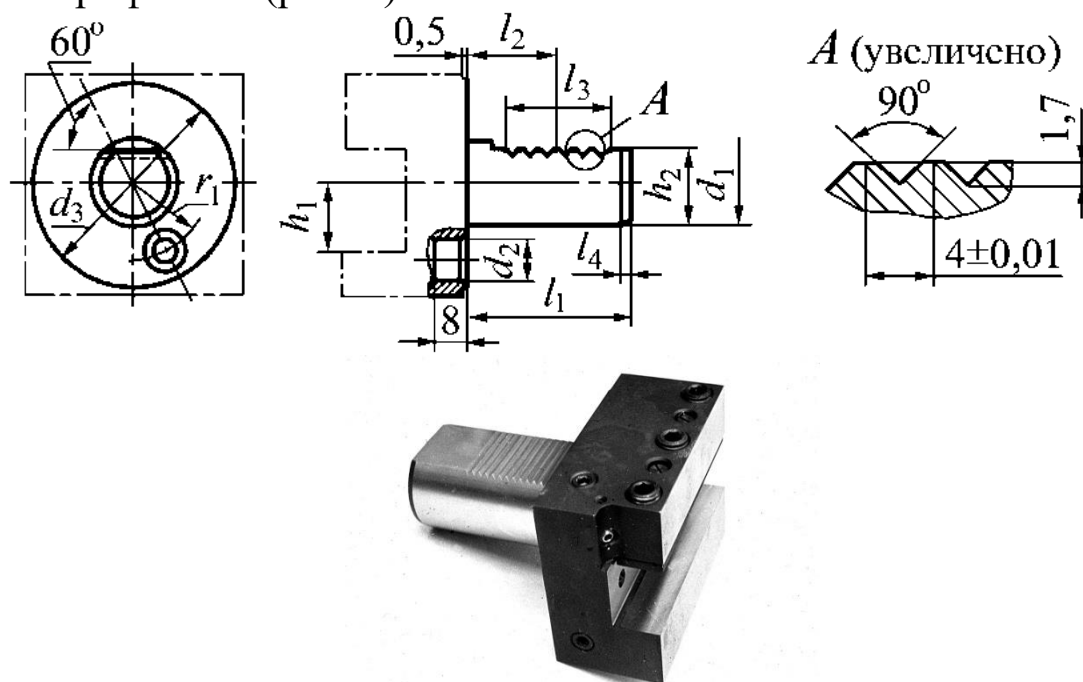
Основные размеры, мм, цилиндрических хвостовиков по ГОСТ 24900–81 и стандарту DIN 69880 для станков токарной группы
